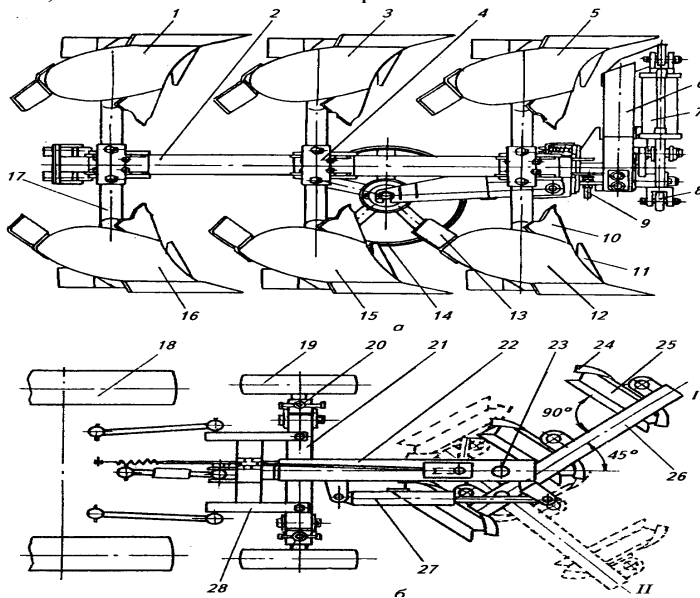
Плуги для гладкой вспашки: а – оборотный ПНО-4-30;
